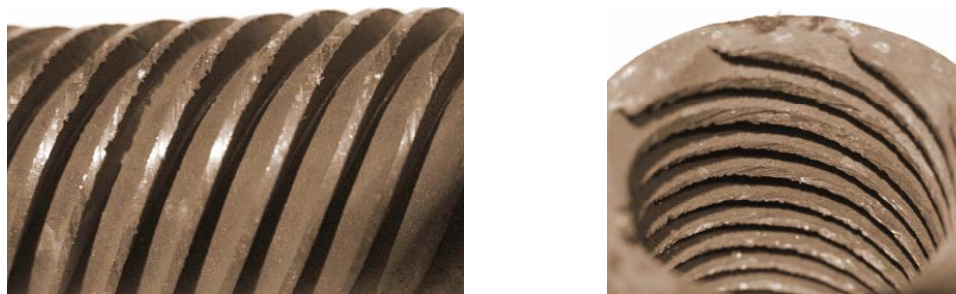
Фотографии втулки вала и втулки подшипника гидростатодинамического подшипника насоса НЦС-04 после испытаний
